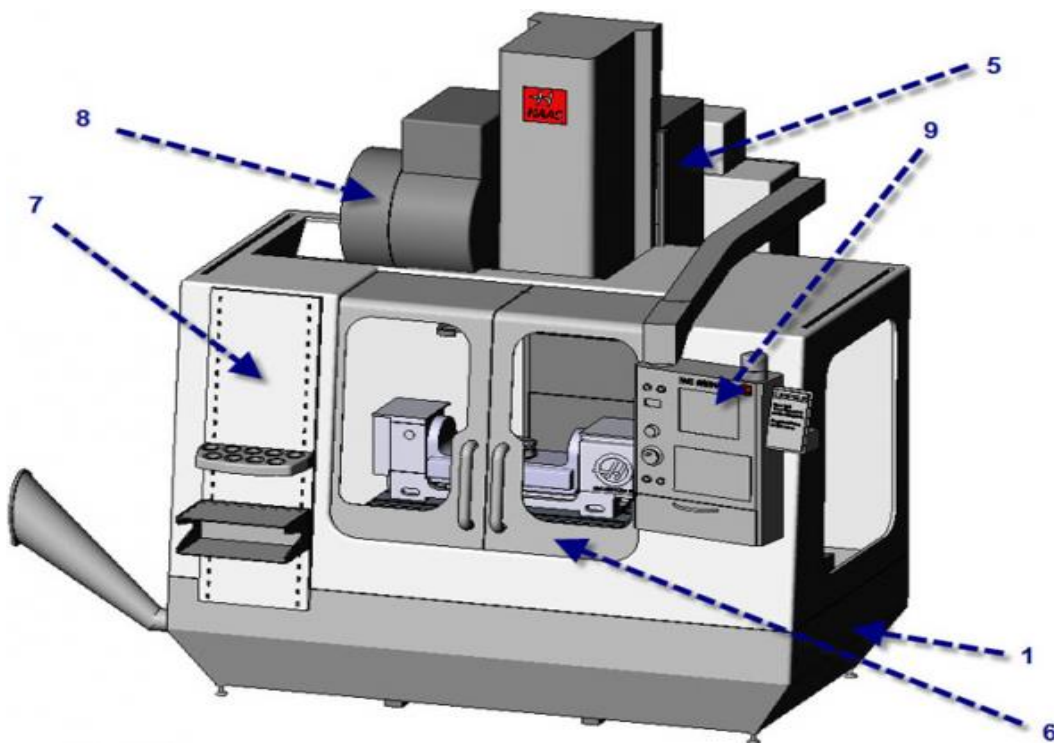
Будова фрезерного верстата з ЧПК
